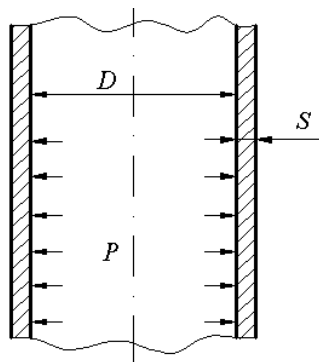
Схема циліндричної обичайки корпусу апарата
